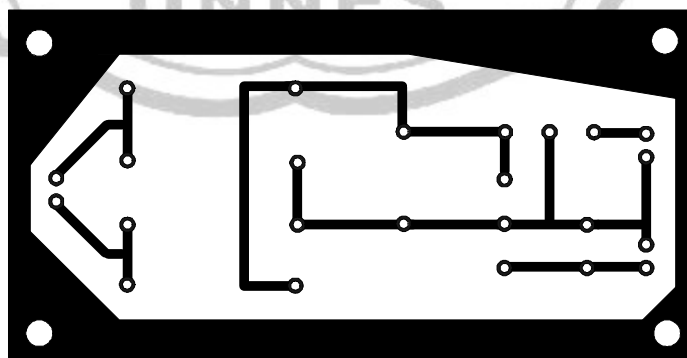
Lay Out Alur PCB Rangkaian Pengendali Motor
